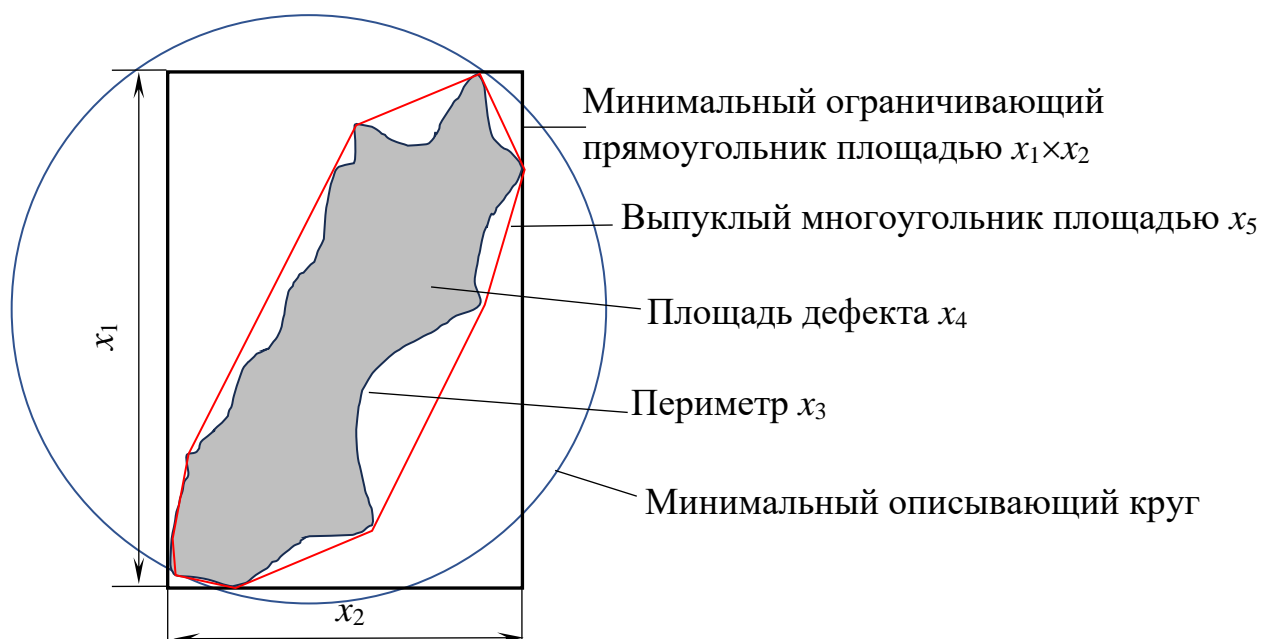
Размерные геометрические признаки дефектов сварного шва
